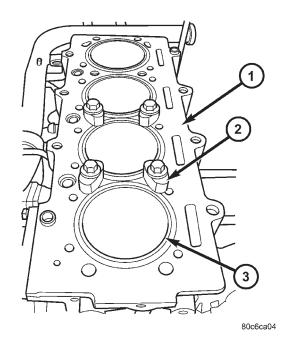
LUGAR DE INMOVILIZACION DE LA CAMISA
